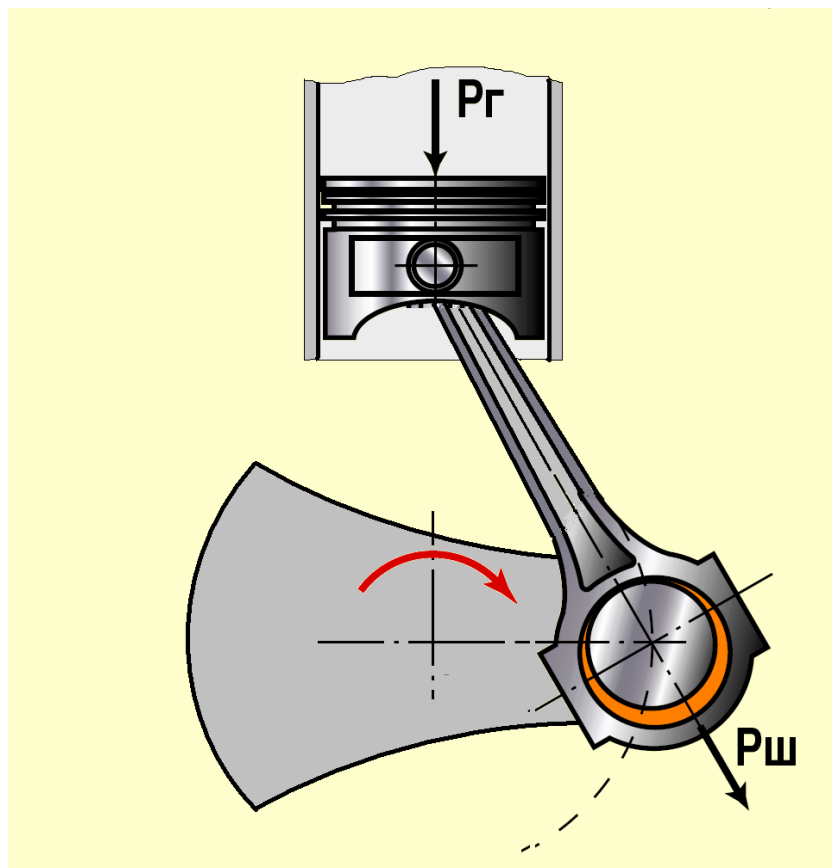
Схема работы кривошипно-шатунного механизма двигателя.
